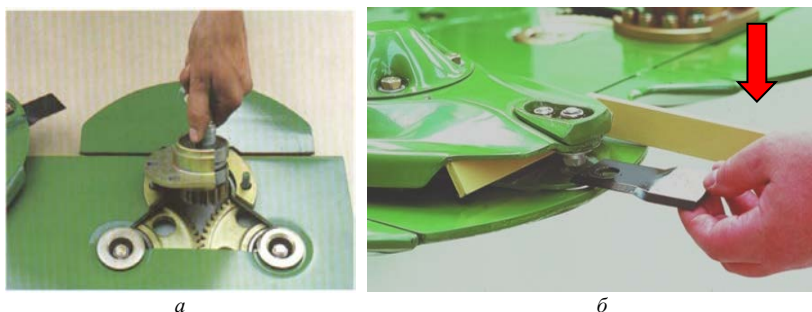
Приемы переналадки косилок фирм Claas и Krone: *а* – переустановка ведомой шестерни ротора; *б* – замена ножа ротора
